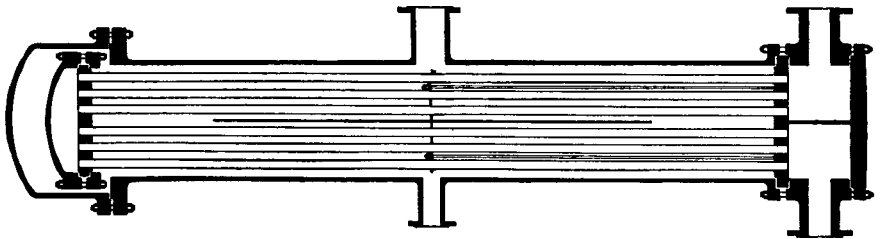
Caldereta horizontal de termosifón. (*Patterson Foundry and Machine Co.*)
